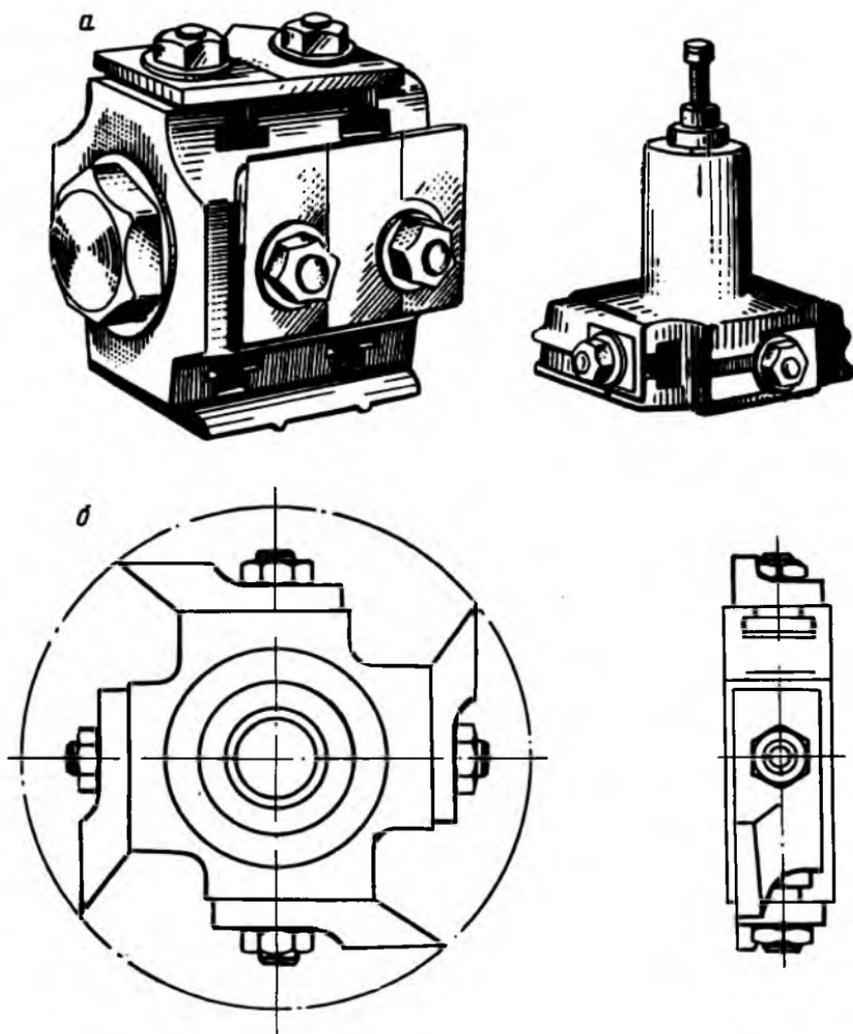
Фрезерные головки с фасонными прямыми резами:
